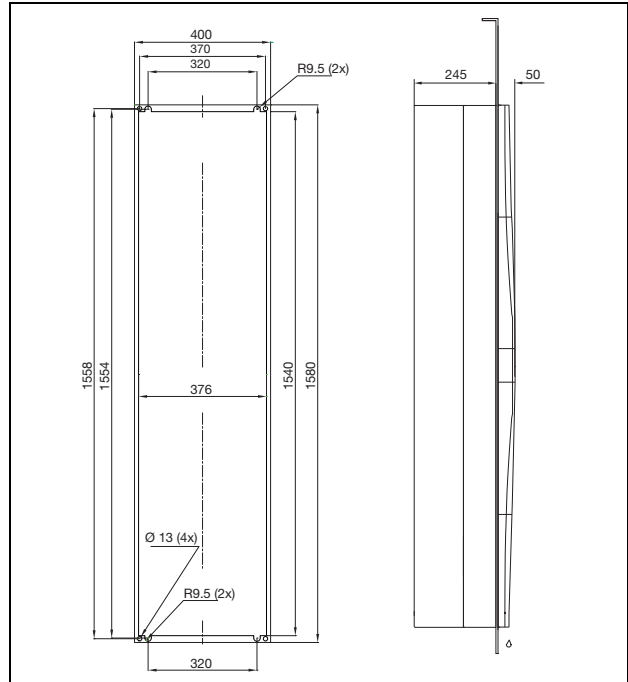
3328.xxx, 3329.xxx утопленный монтаж
